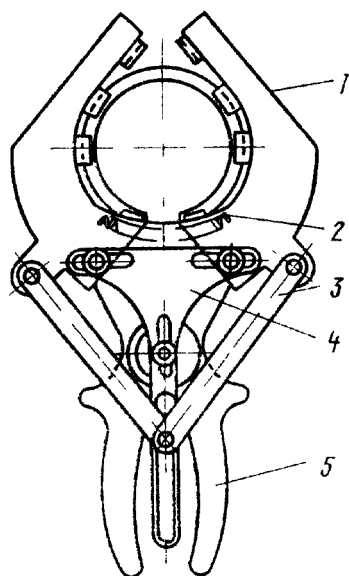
Съёмник для снятия и установки поршневых колец компрессора:
